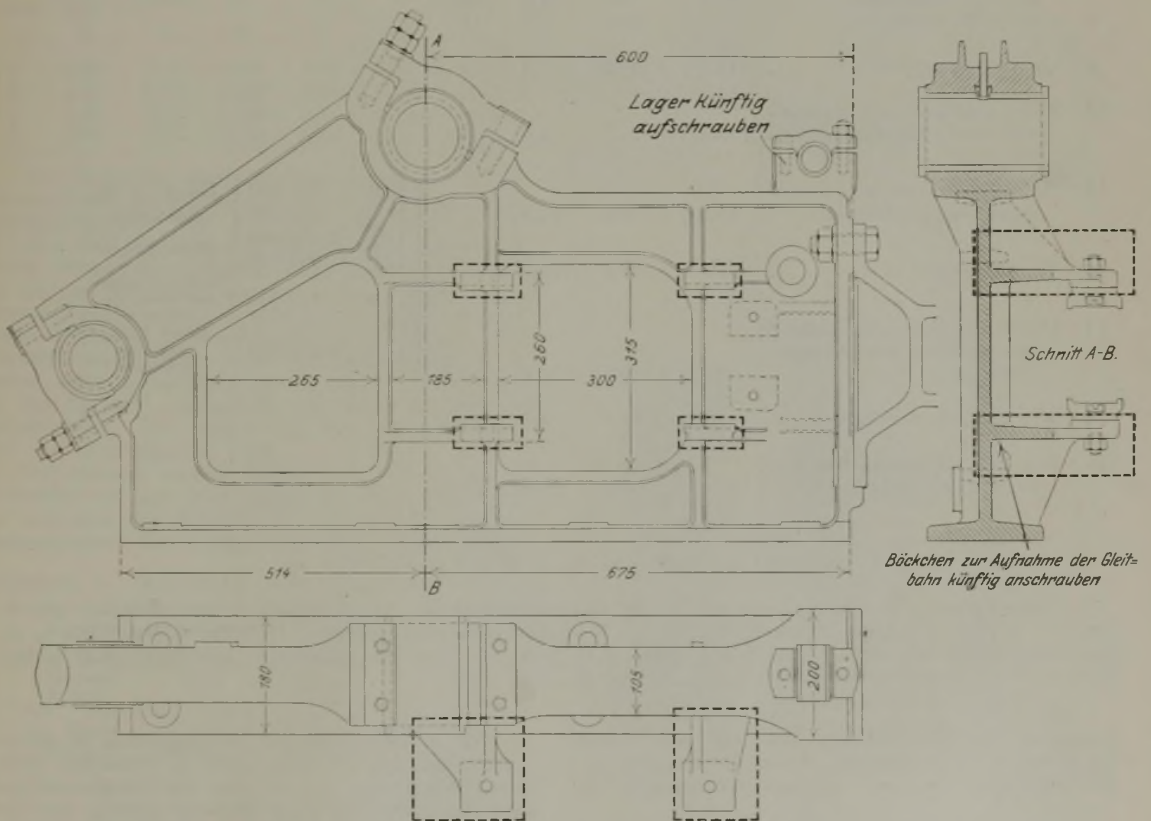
Maschinenrahmen für Schiffsladewinden.
